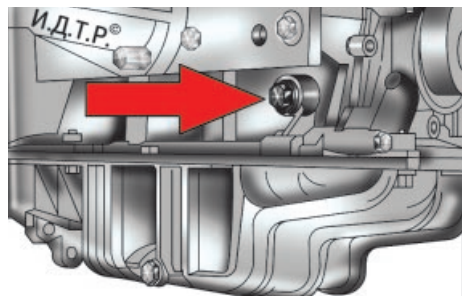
Заглушка отверстия для установки фиксирующего стержня коленчатого вала
